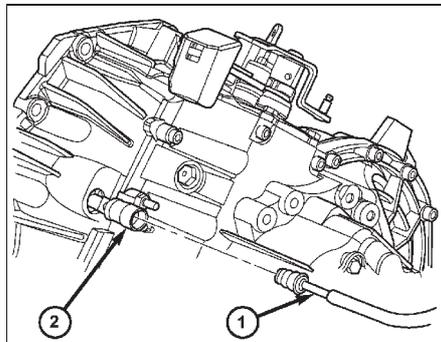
Исполнительный цилиндр привода сцепления. 1 - трубка главного цилиндра, 2 - исполнительный цилиндр.
